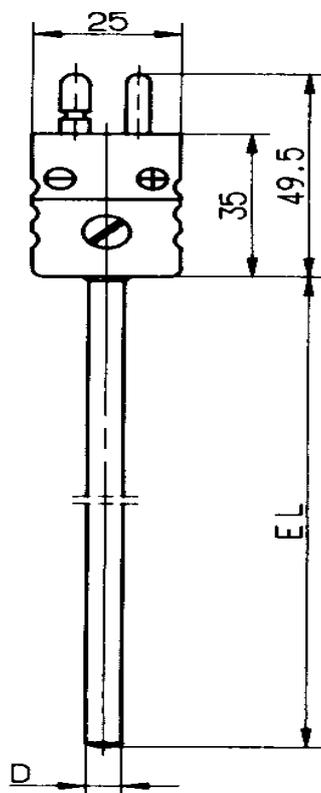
铠装(矿粉隔离)型热偶外形尺寸 3
